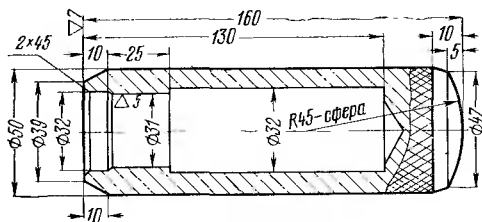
Оправка для напрессовки внутреннего кольца подшипника на винт рулевого управления
